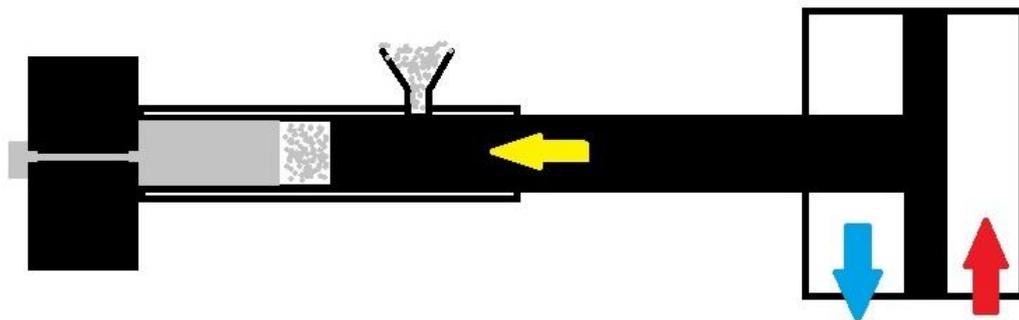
Imagem do pistão numa máquina de Injeção em Moldes.
